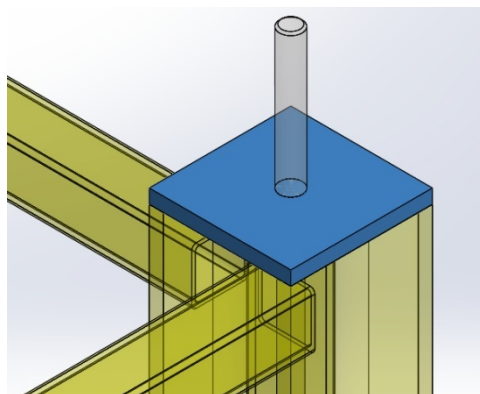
Tapa cuadrada 100x100x10mm con perno soldado
